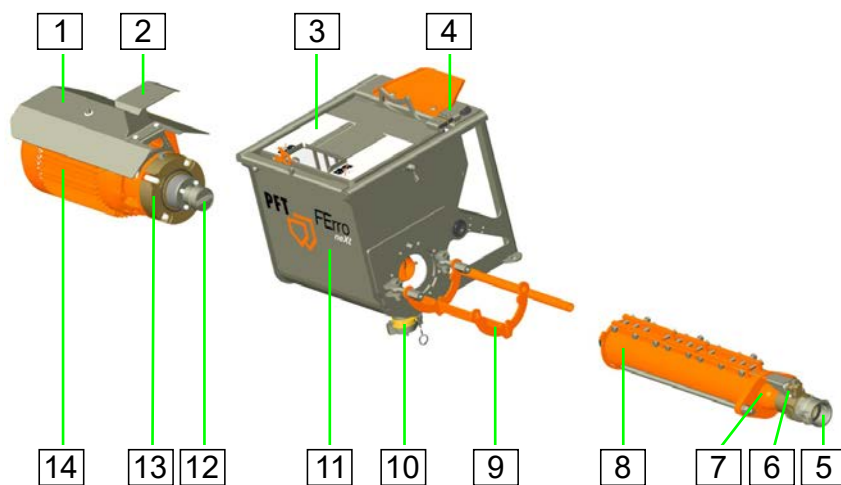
Baugruppe Pumpenmotor mit Behälter und Pumpe
